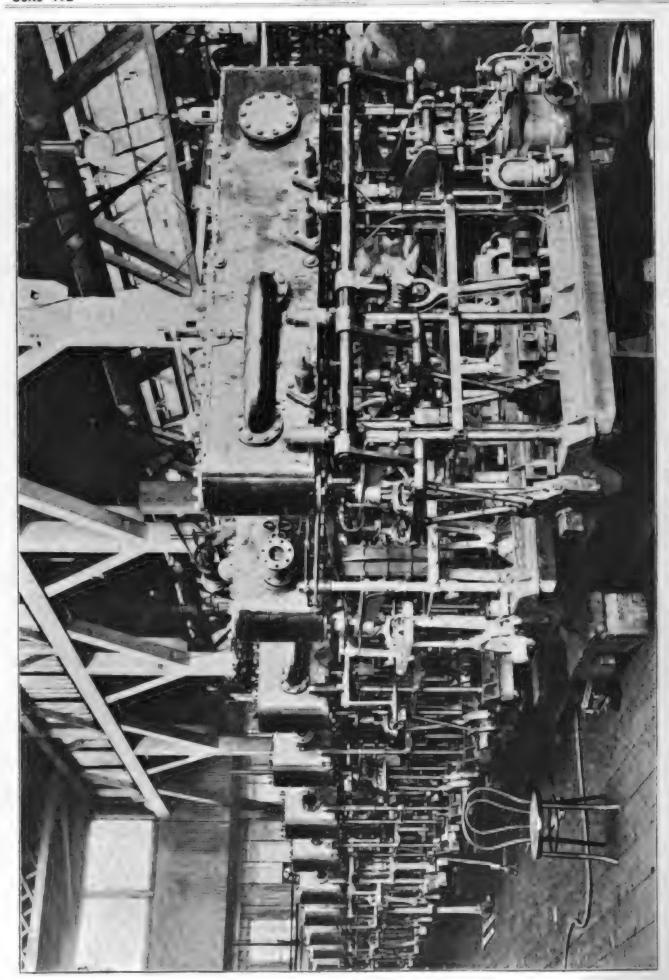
Maschine für einen Doppelschrauben-Fährdampfer für Kalkutta, gebaut von John J. Thornycroft & Co. in Chiswick
